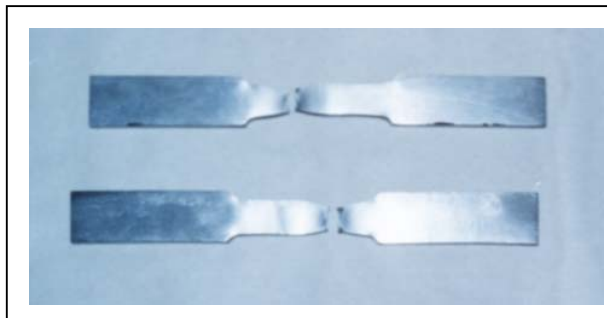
PROBETAS DE TENSIÓN CON SECCIÓN REDUCIDA
